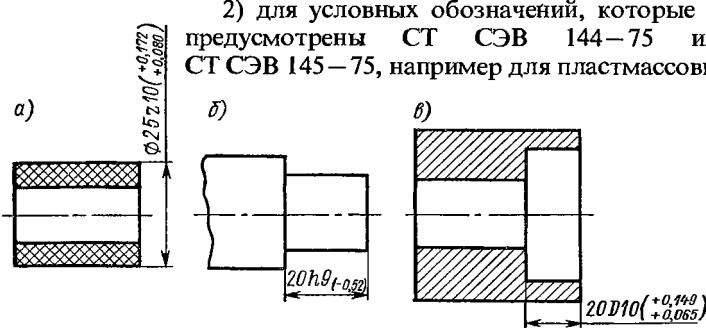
Нанесение предельных отклонений размеров: а – пластмассовых деталей; б, в – уступов с несимметричным полем допуска
